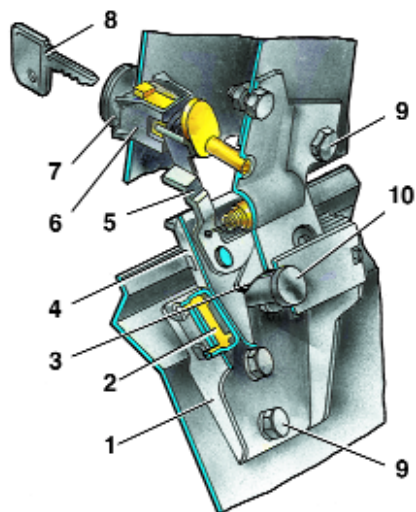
Замок и привод замка двери задка: 1 – защелка замка двери задка; 2 – буфер защелки; 3 – вилка замка; 4 – замок двери задка; 5 – фиксатор вилки замка; 6 – держатель выключателя замка двери задка; 7 – выключатель замка двери задка; 8 – ключ; 9 – болт крепления замка и защелки; 10 – палец защелки
